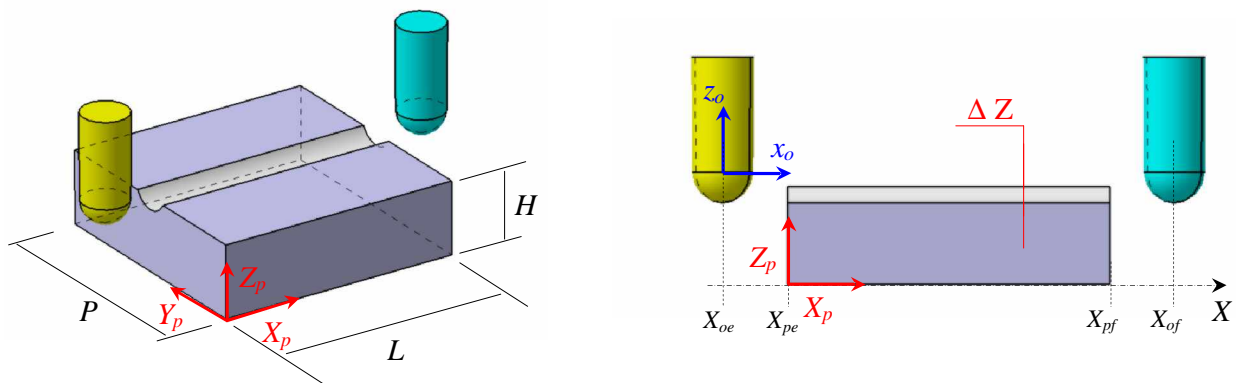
Géométrie de la pièce et positionnement de l'outil par rapport à la pièce.
